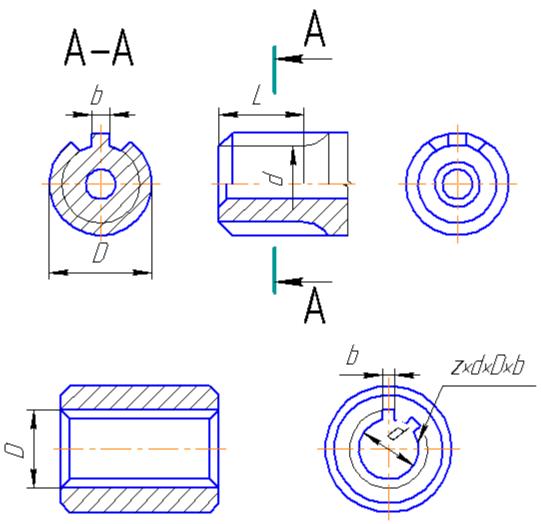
Пример детали со шлицевым хвостовиком и фрагменты чертежей деталей
